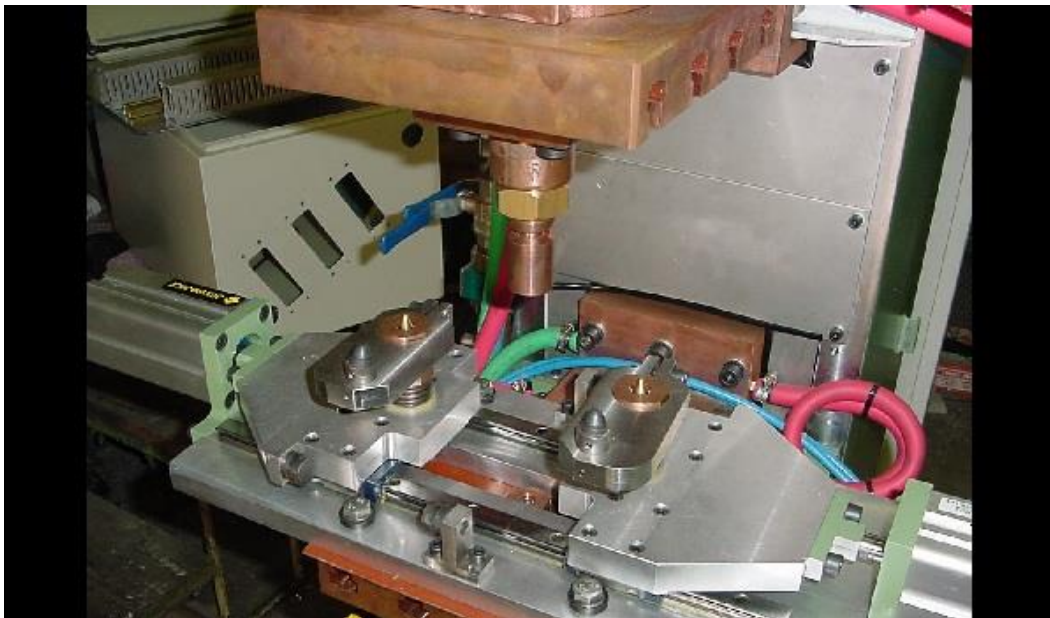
Máquina de pedestal para soldar por puntos tipo prensa.
